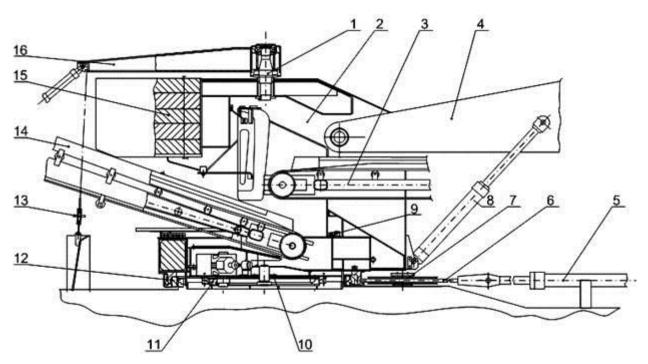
Поворотный механизм: 1- ось; 2- клеть; 3- основной конвейер; 4- стрела ротора; 5, 8- гидроцилиндр; 6- канат; 7- блок; 9- концевой выключатель; 10- основание; 11, 12- опора роликовая; 13- устройство натяжное; 14- поворотный конвейер; 15- противовес; 16- поворотная стрела
